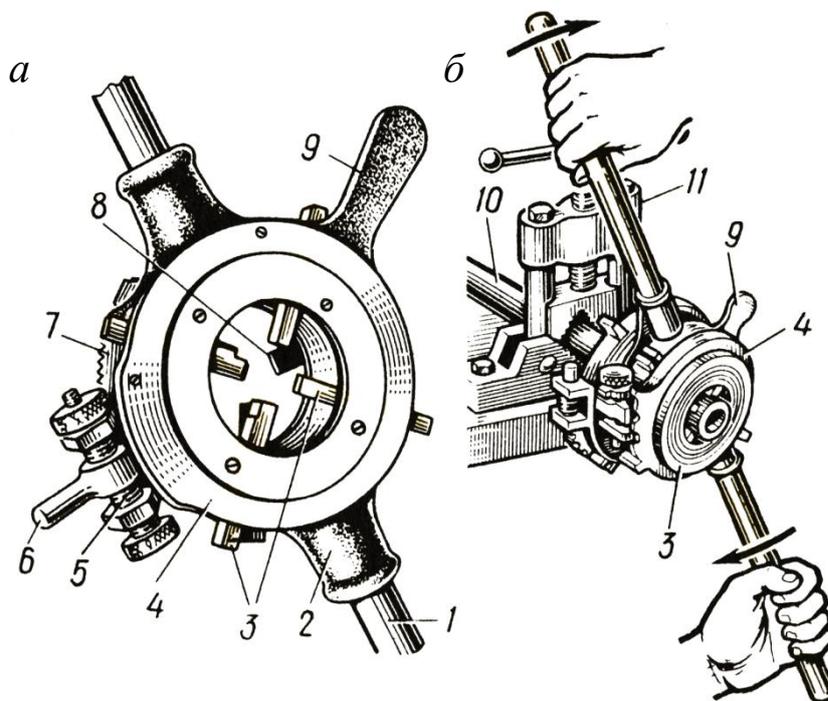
Клупп трубный для резьб размером от $\frac{1}{2}$ " до 2" с раздвижными плашками:
